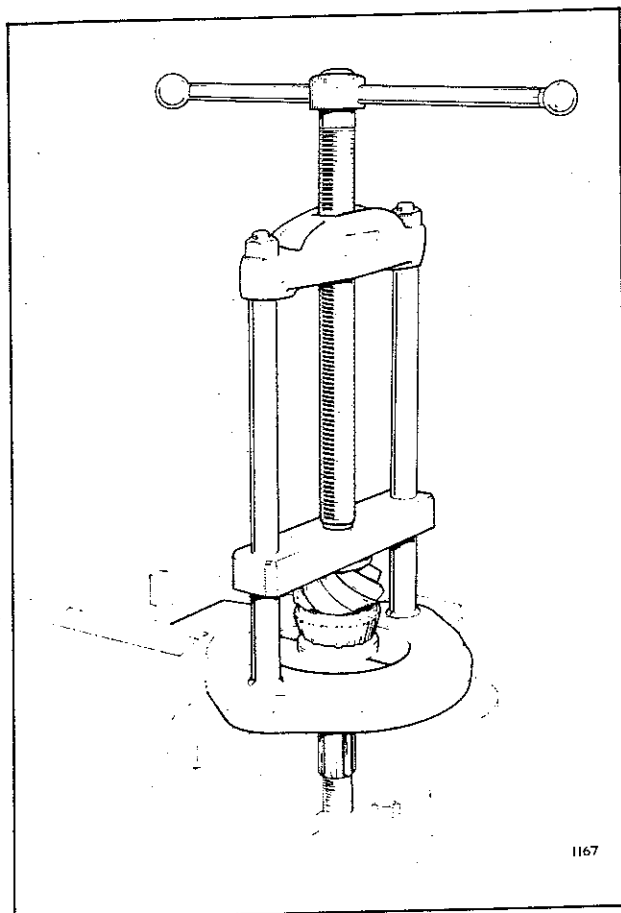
Remontage des cales et du roulement intérieur sur le pignon
